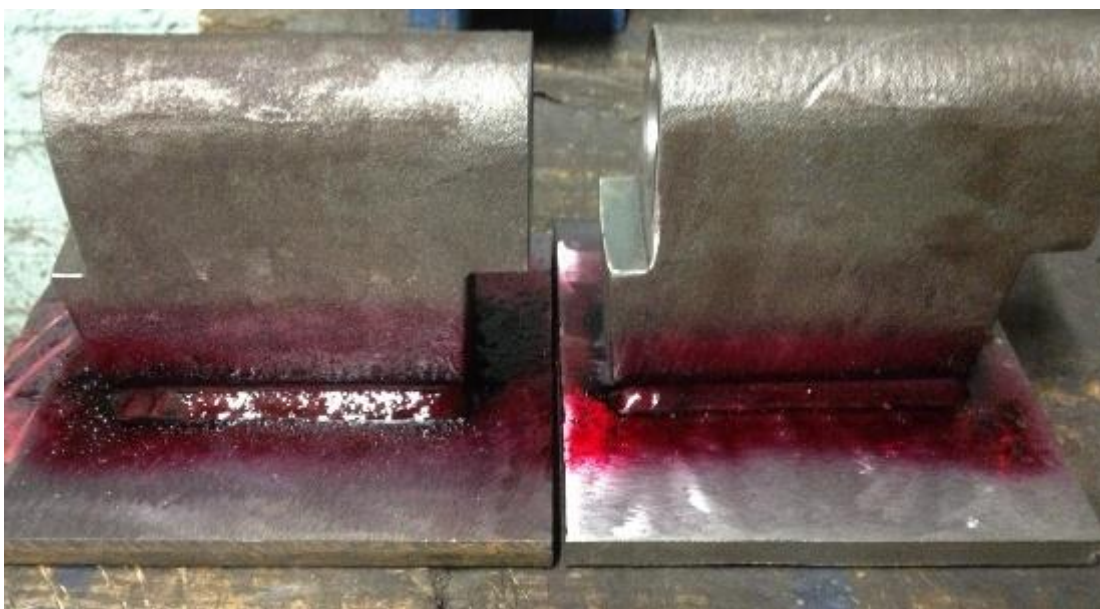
Aplicação do líquido penetrante nas juntas soldadas
